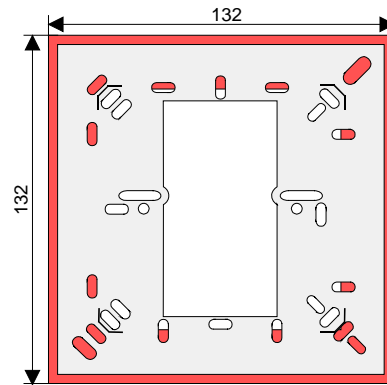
Marco de montaje universal (Art.-Nr. 704967)
